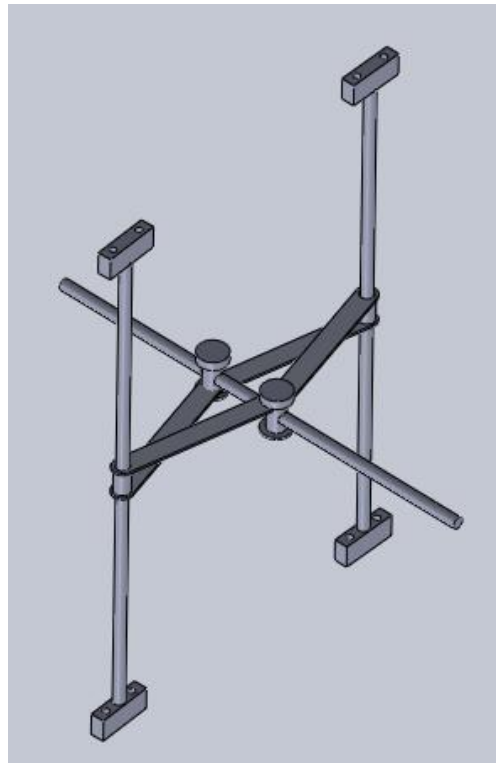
Mecanismo articulado para espaçador de quatro cabos .
